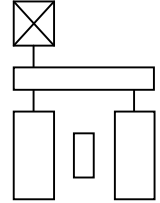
Схема привода трехочагового прокатного модуля для условий промежуточной и чистовой групп сортовых станов со станинными приводными валками:
